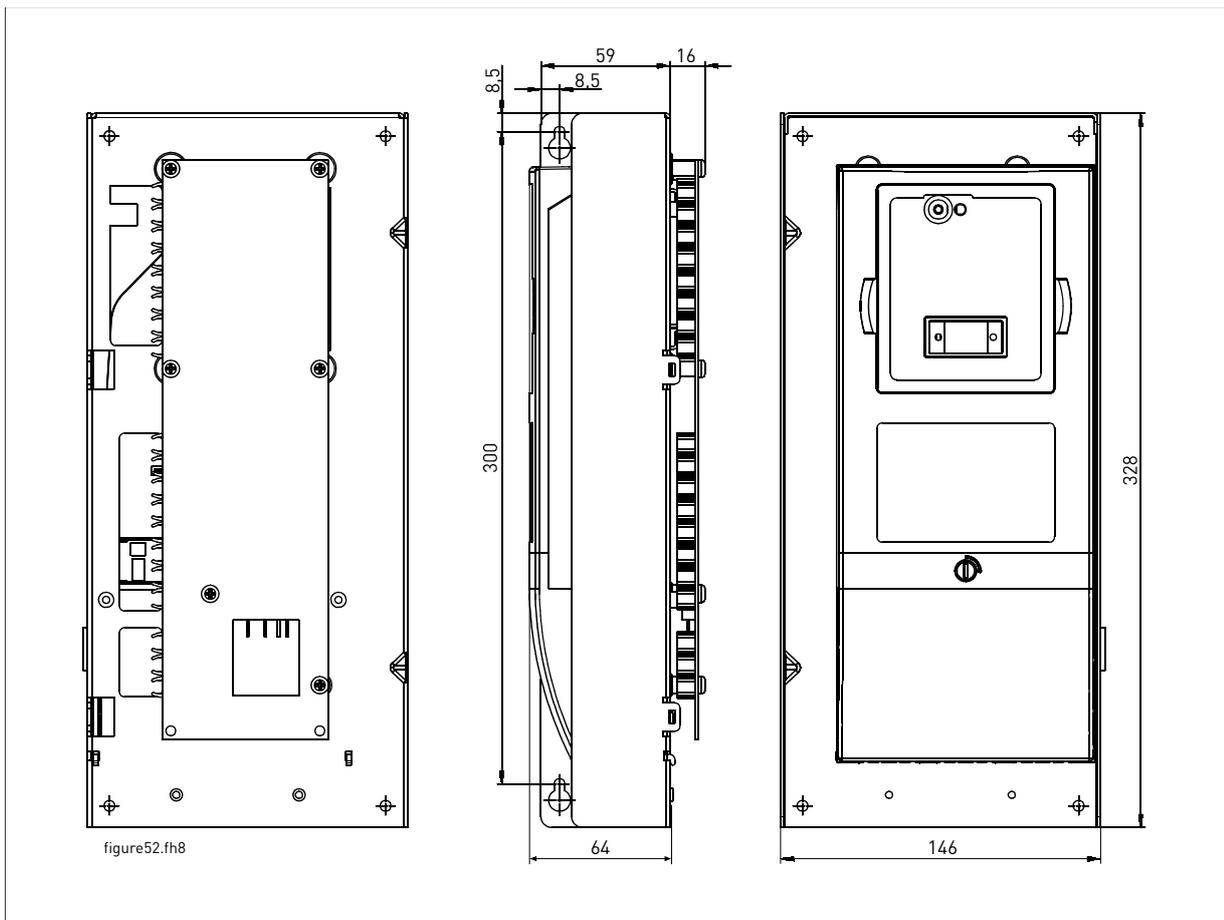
Abmessungen der Steuereinheit (mit Star Coupler Board angeschlossen – nur FR12 bzw. FR14)
